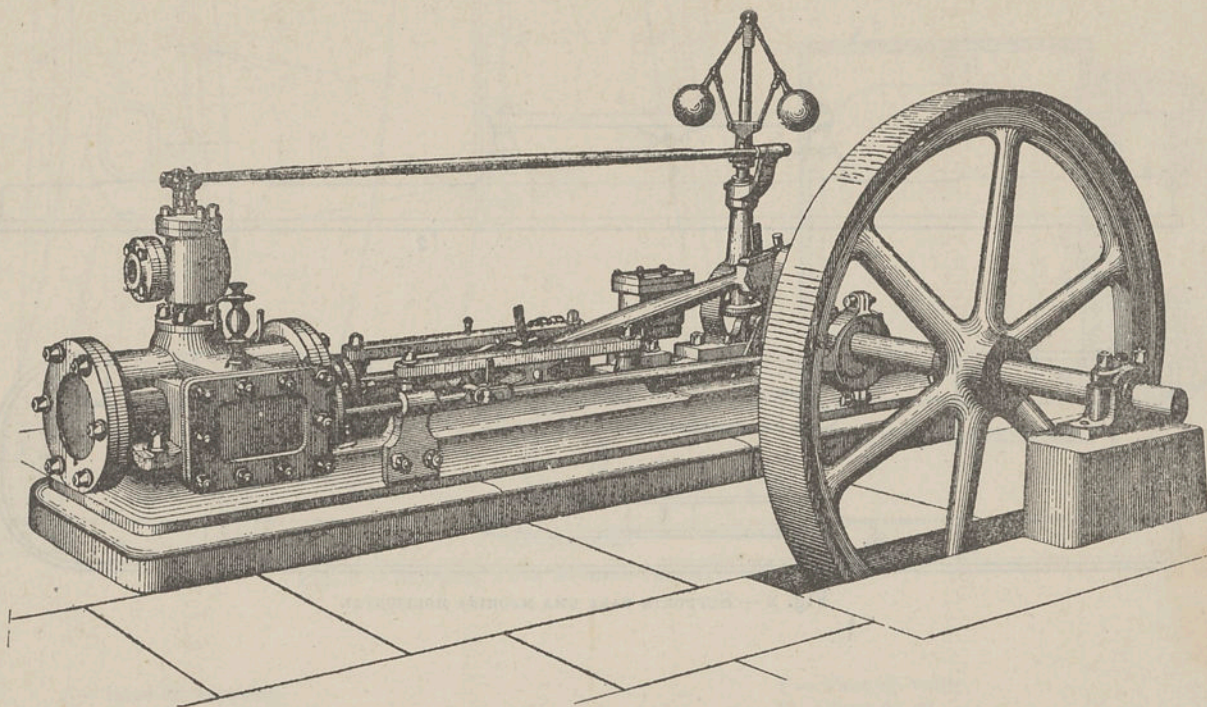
MACHINA HORIZONTAL DE TIRANTE DIRECTO
